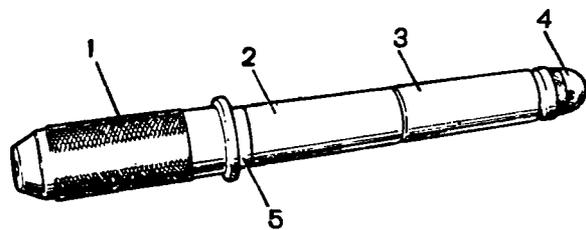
Установка поршневого пальца на приспособление А.60325 для запрессовки: 1 - валик приспособления; 2 - поршневой палец; 3 - направляющая; 4 - упорный винт; 5 - дистанционное кольцо
